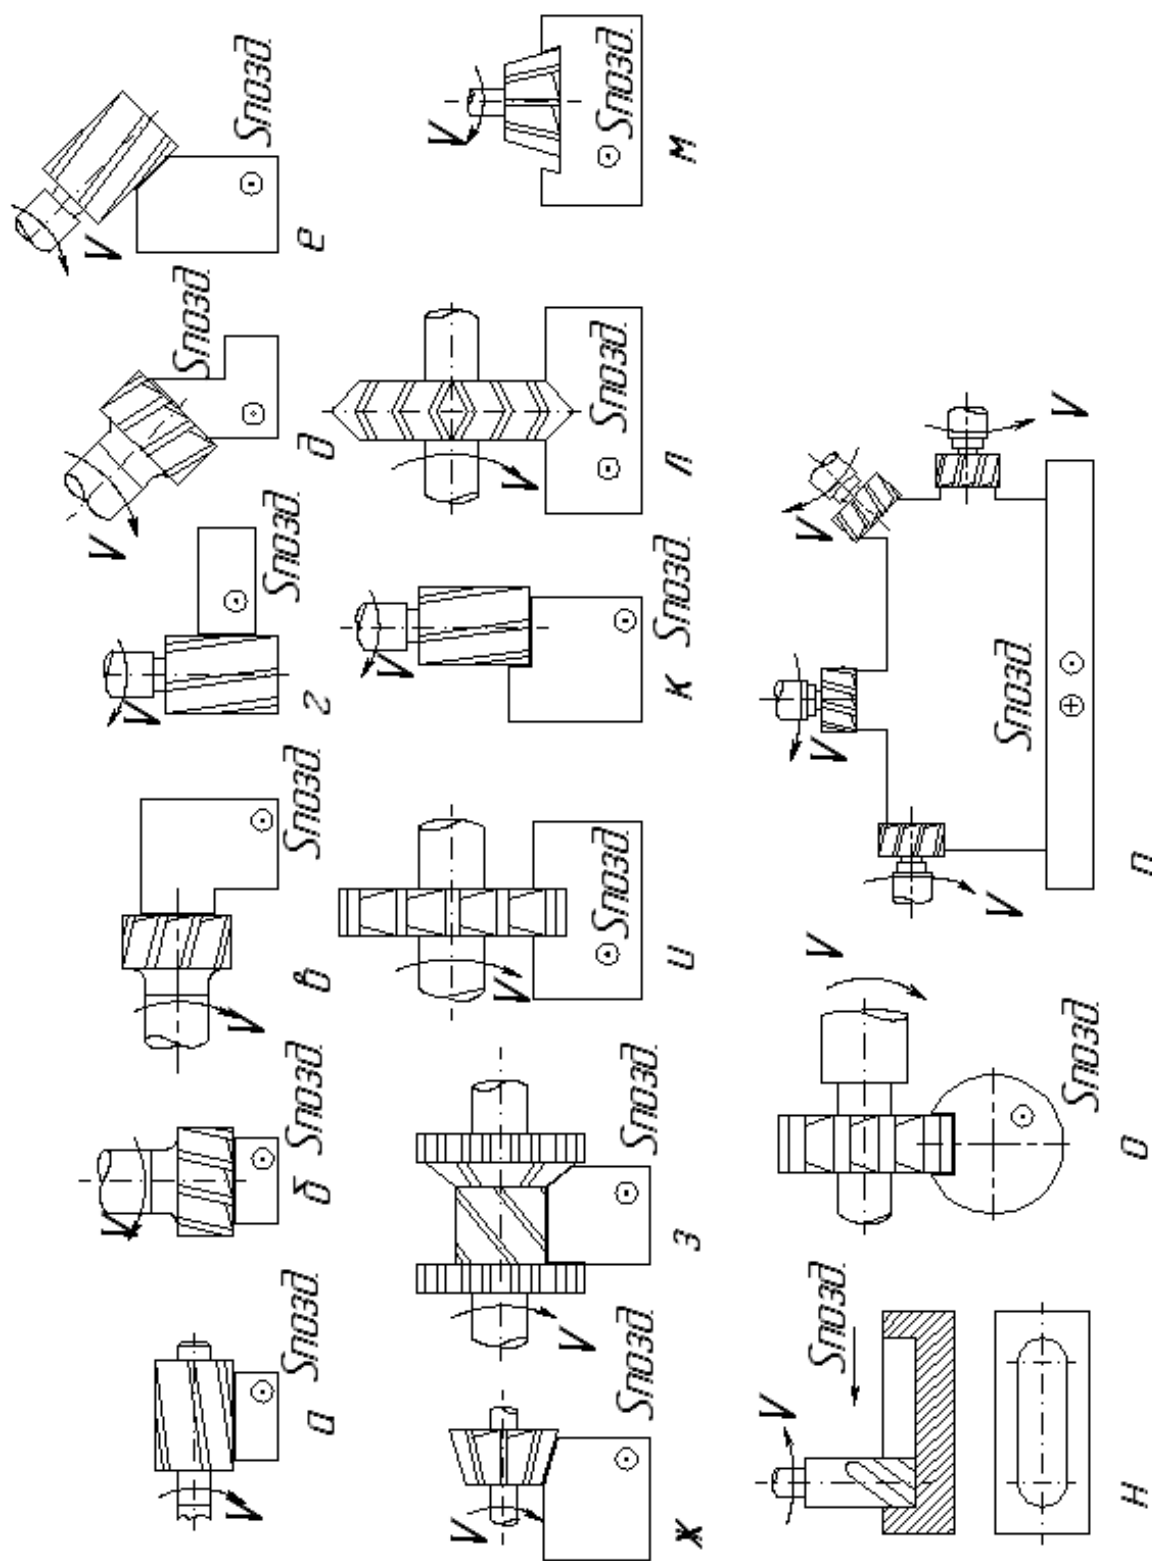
Види обробок, виконуваних на фрезерних верстатах
